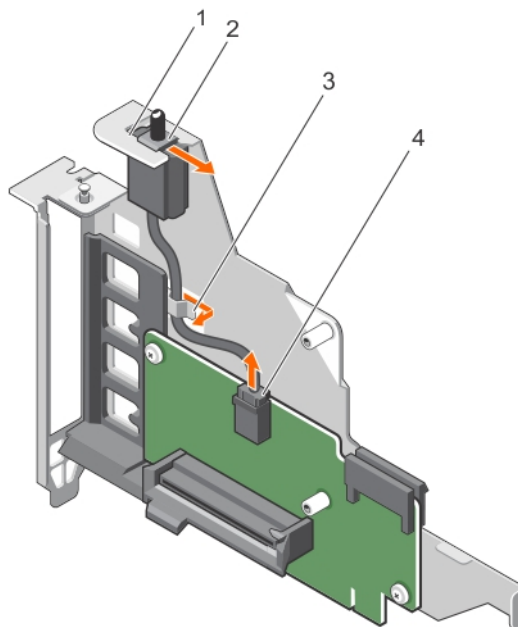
Entfernen des Gehäuseeingriffsschalters
